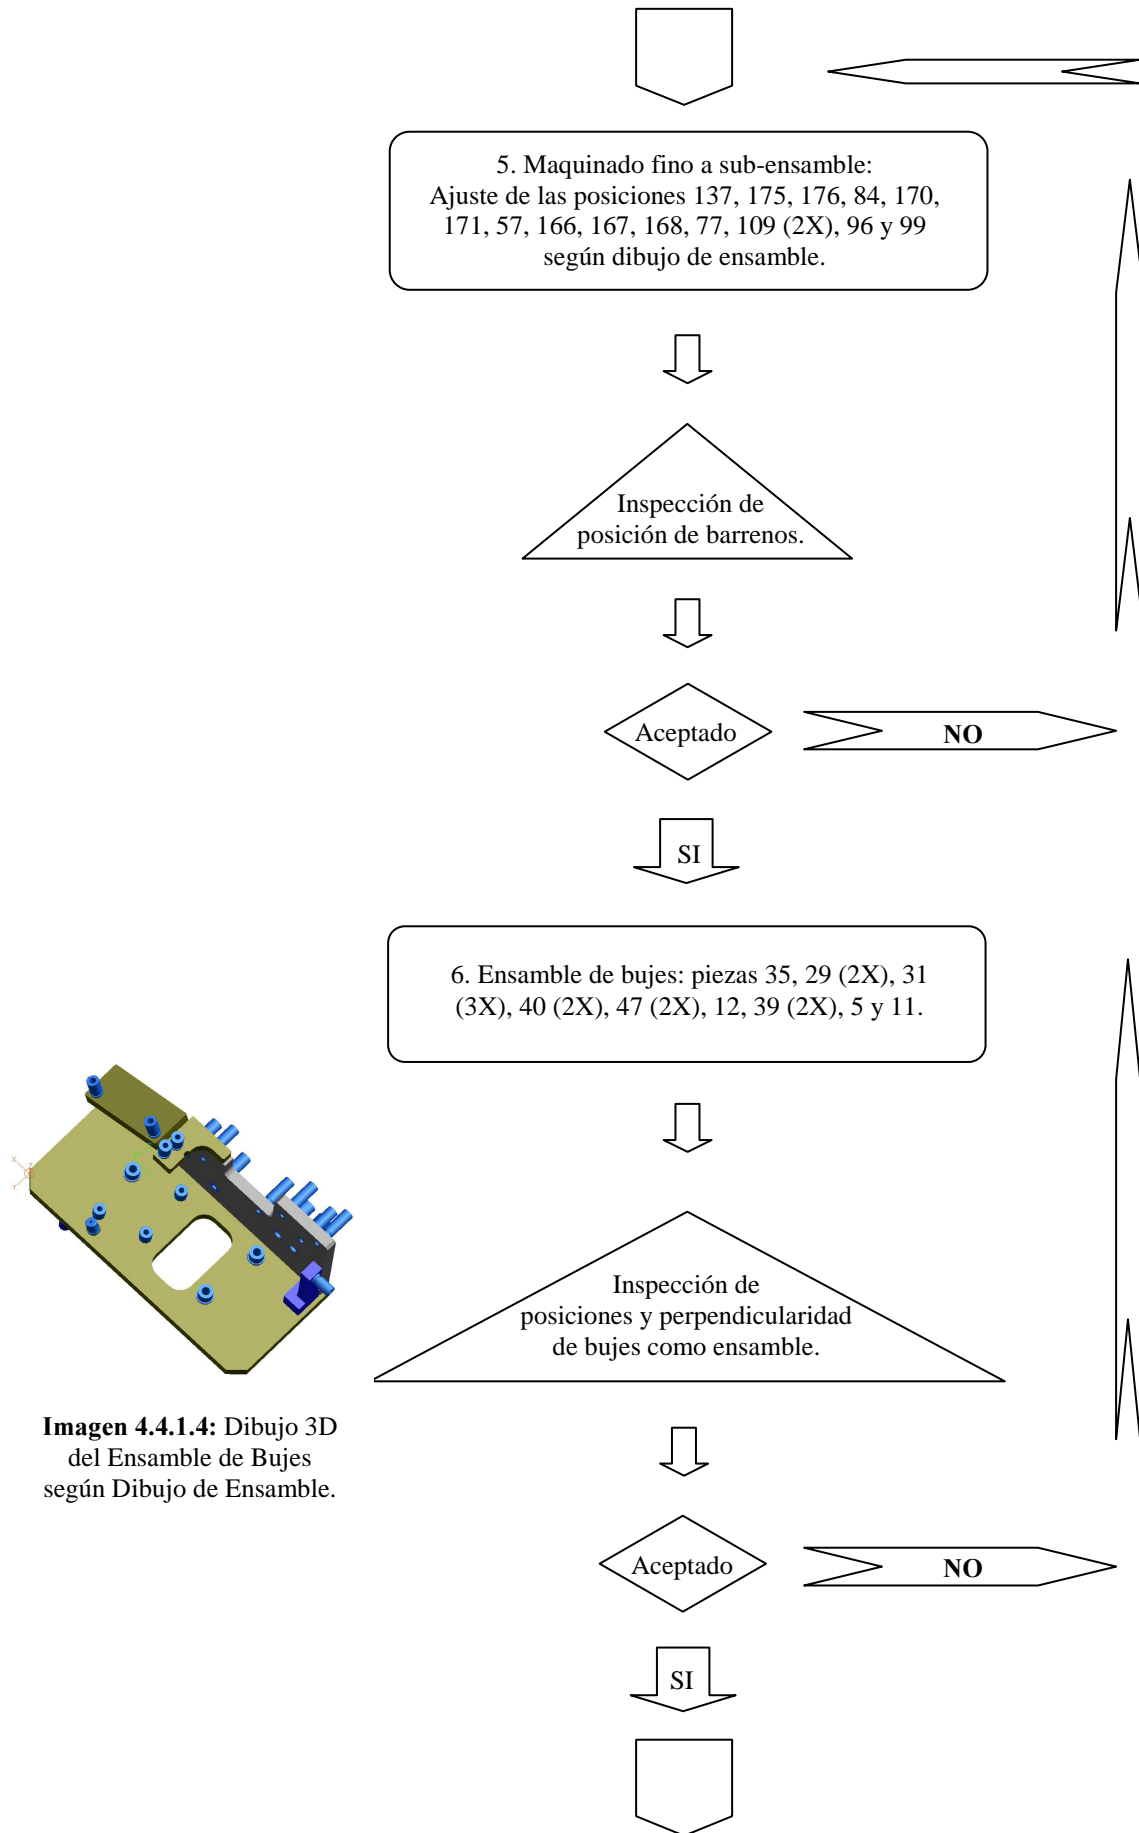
Dibujo 3D del Ensamble de Bujes según Dibujo de Ensamble.
